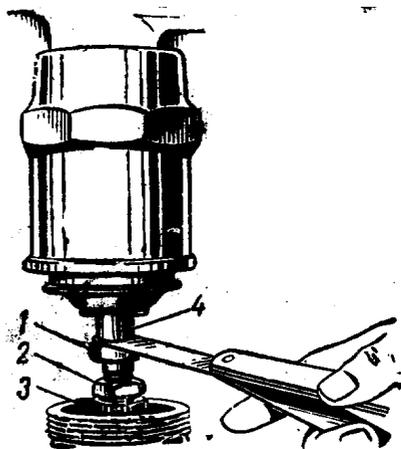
Регулировка клапанных зазоров мотоцикла Харлей-Давидсон: 1 — регулировочный болт; 2 — контргайка регулировочного болта; 3 — толкатель; 4 — стержень клапана
